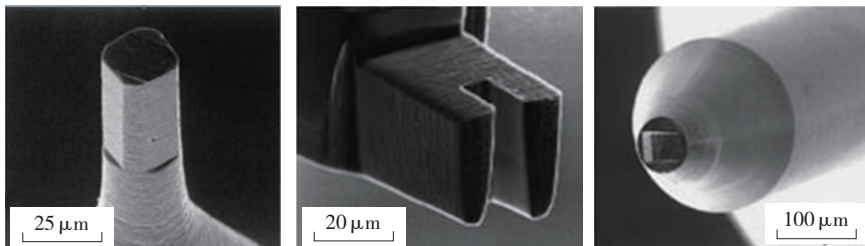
美国桑迪亚国家实验室研制的异型微细切削刀具
